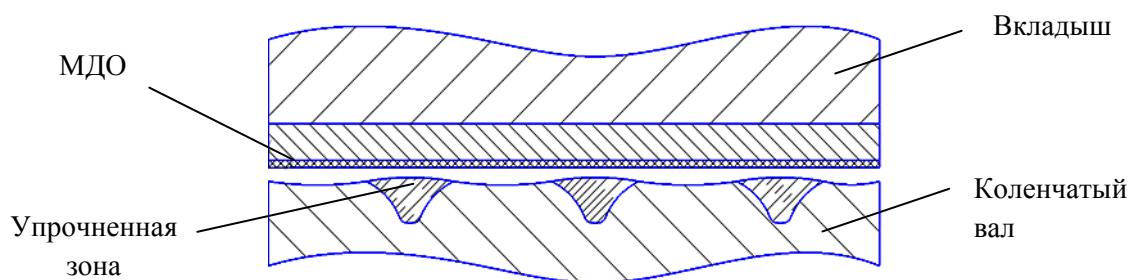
Схема взаимодействия рабочих поверхностей шейки коленчатого вала и сталеалюминиевого вкладыша
